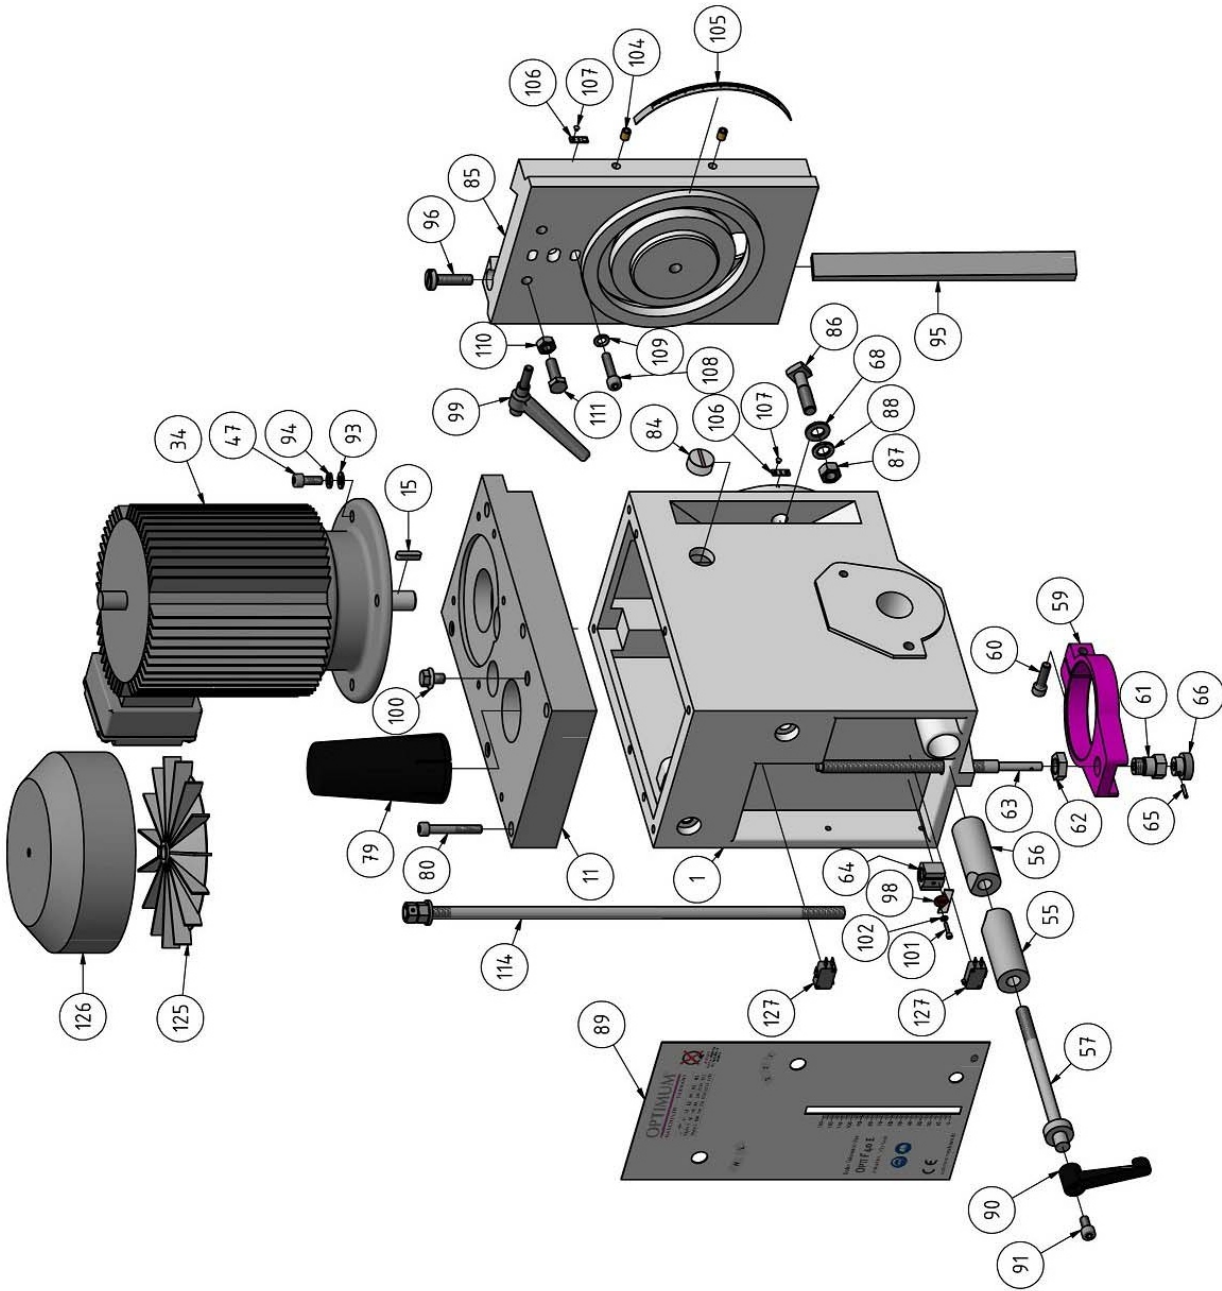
Fräskopf 6 von 6 - Cabezal fresador 6 de 6
